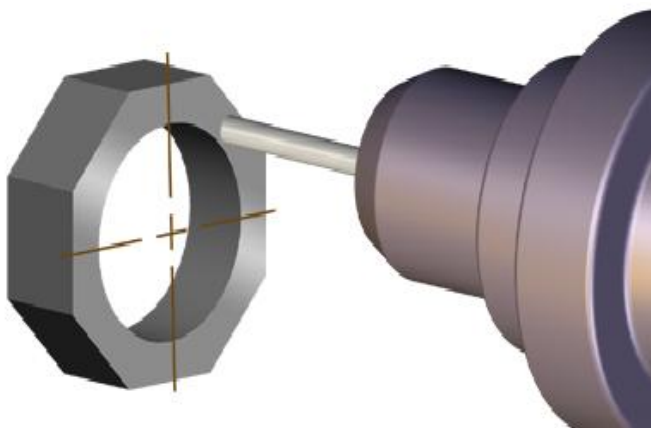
Obrábění tvaru pomocí osy C a v axiálním směru
